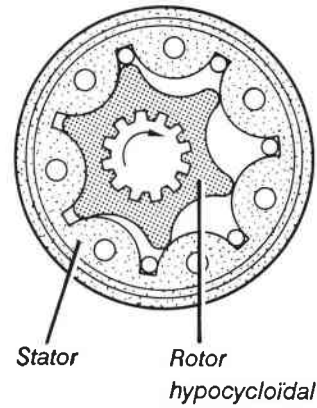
Moteur hydraulique à rotor hypocycloïdal.
